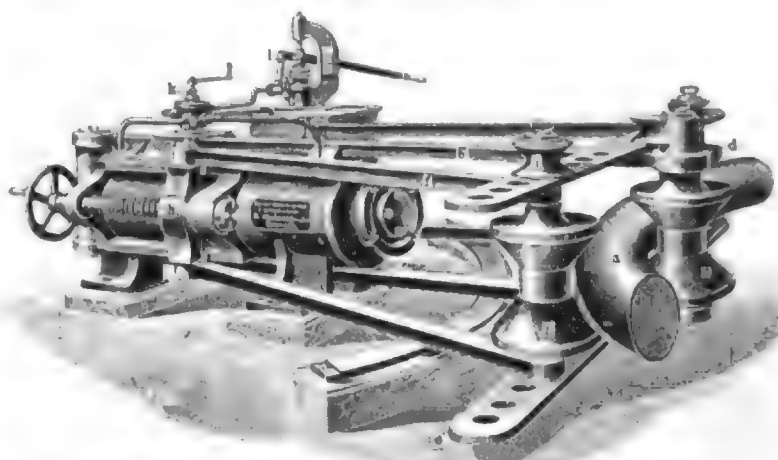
Hydraulische Rohrbiegemaschine von der Bonner Maschinenfabrik und Eisengießerei Fr. Mönkemöller & Cie. in Bonn-Dottendorf.
